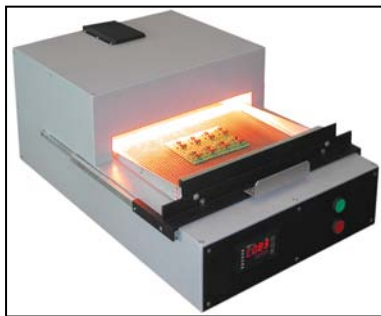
Печь для оплавления паяльной пасты. Общий вид
